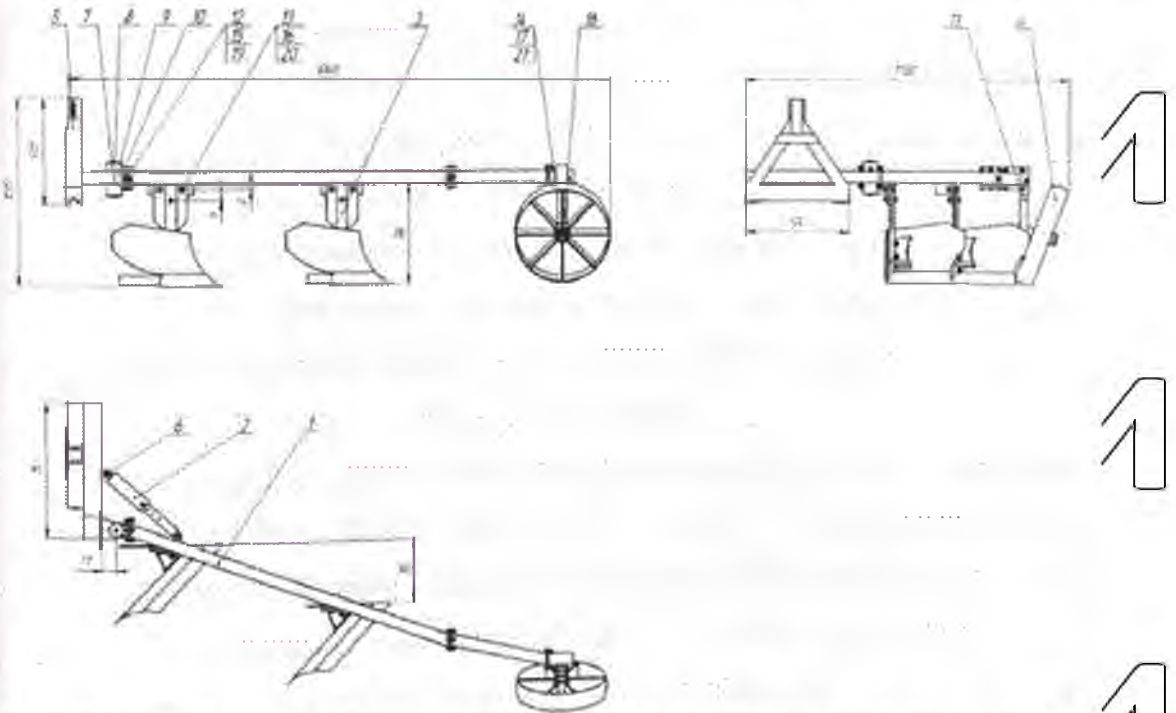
Передньоначіпний плуг з шарніром. Загальний вигляд
